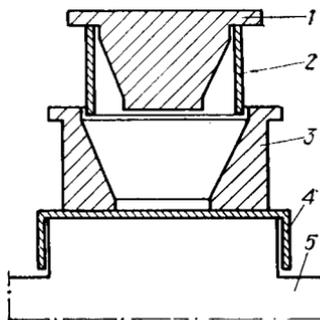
Приспособление для штамповки переходов: 1 — пуансон; 2 — трубная заготовка; 3 — матрица; 4 — короб-ограничитель; 5 — основание молота.
